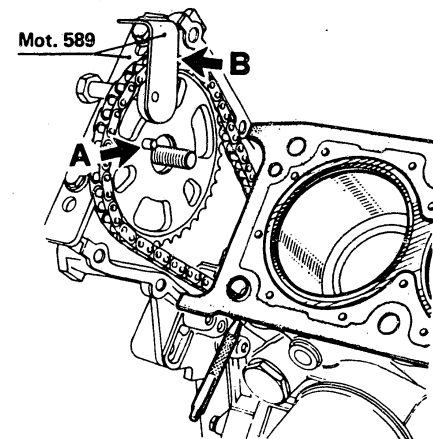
Motor Z7V: A der nach oben stehende Arretierstift des Nockenwellenrades, B das Spezialwerkzeug, mit dem das Kettenrad bei ausgebautem Zylinderkopf am Stirnradgehäuse befestigt wird.
